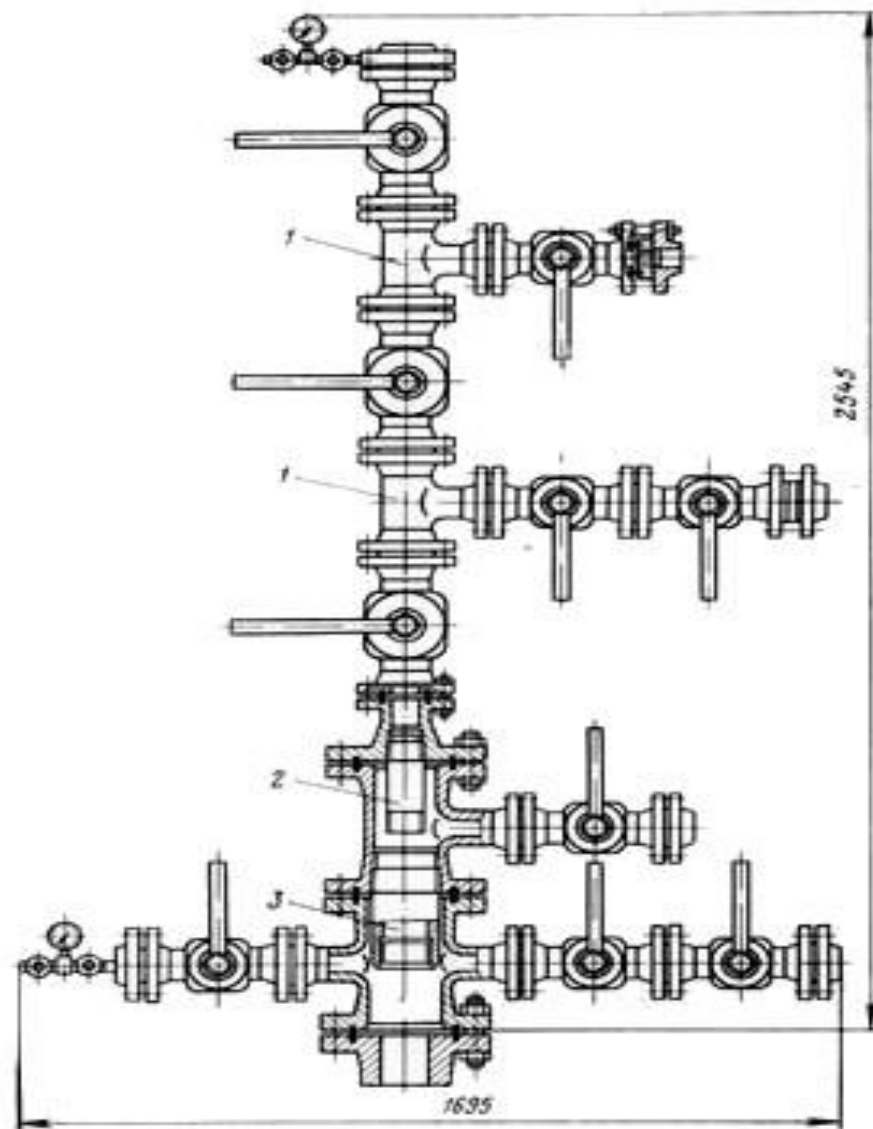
Фонтанная крестовая арматура (4АФК-50-700) высокого давления (70 МПа) для однорядного подъемника: 1 - вентиль, 2 - задвижка, 3 - крестовина, 4 - катушка для подвески НКТ, 5 - штуцер, 6 - крестовины ёлки, 7 - буфер, 8 - патрубок для подвески НКТ, 9 - катушка
